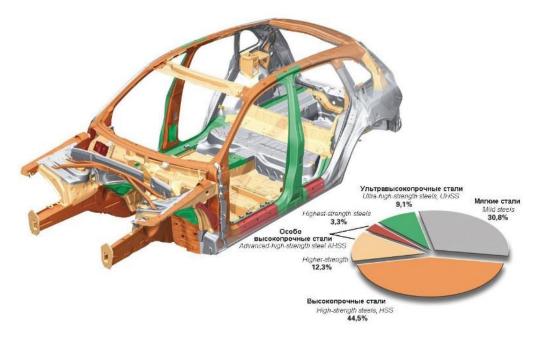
Соотношение сталей, применяемых для изготовления автомобиля
